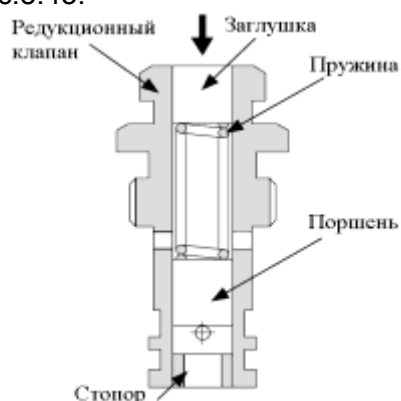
Редукционный клапан топливонасоса ТНВД VE.
